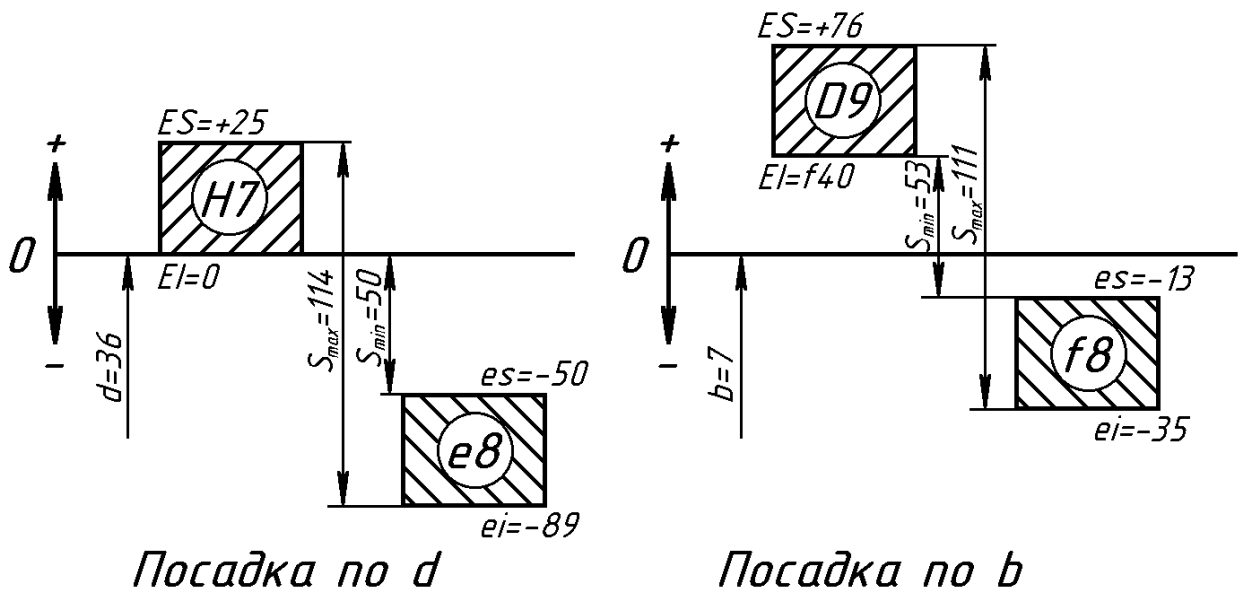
Схемы расположения полей допусков шлицевого соединения
